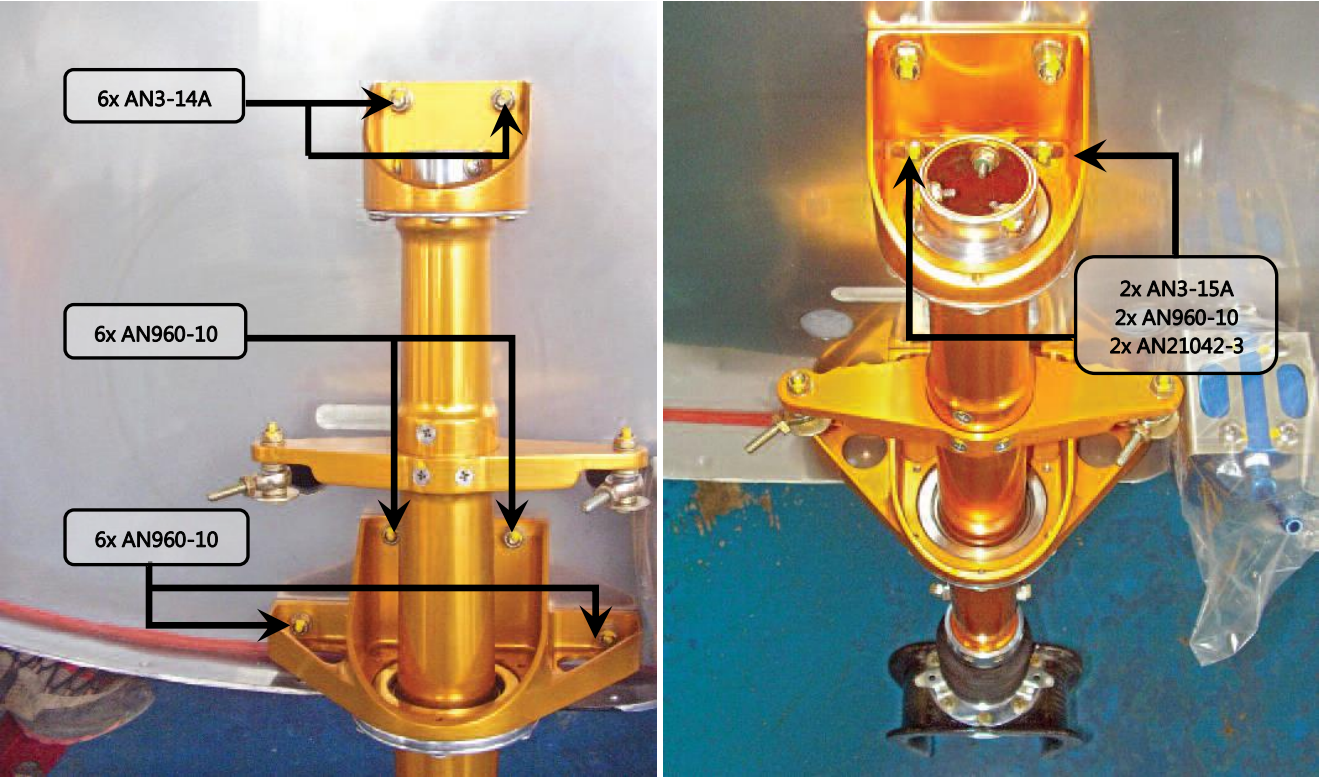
Fixação da Estrutura da Bequilha
